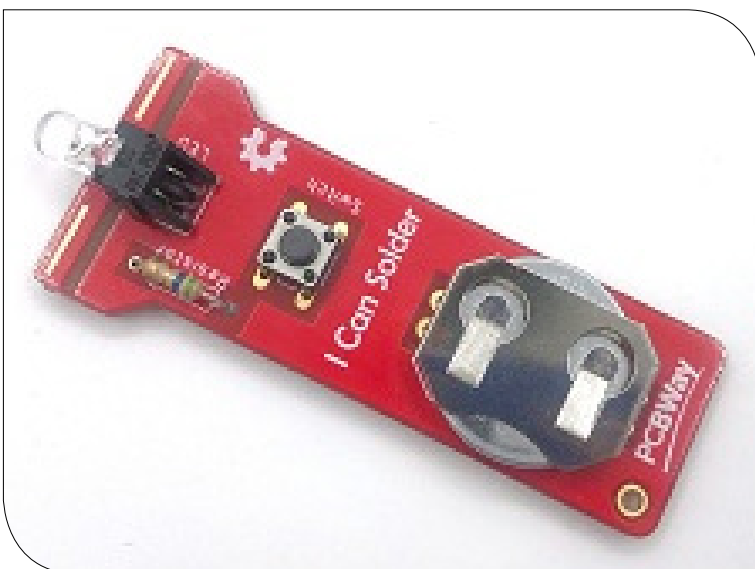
PCB LED di PCBWay (Fonte: PCBWay)
